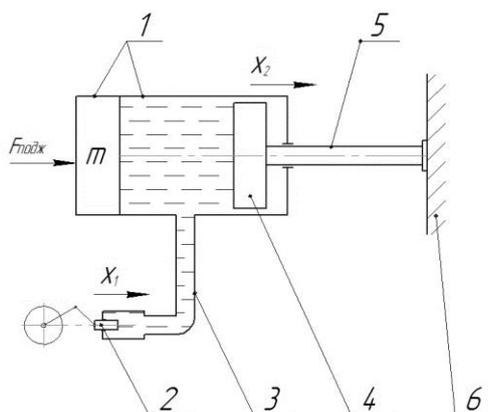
Принципиальная схема гидроимпульсного силового механизма: 1 – корпус гидроцилиндра с активной массой; 2 – плунжер; 3 – рукав высокого давления (РВД); 4 – поршень; 5 – бурильный инструмент (штанга); 6 – разрушаемая порода
